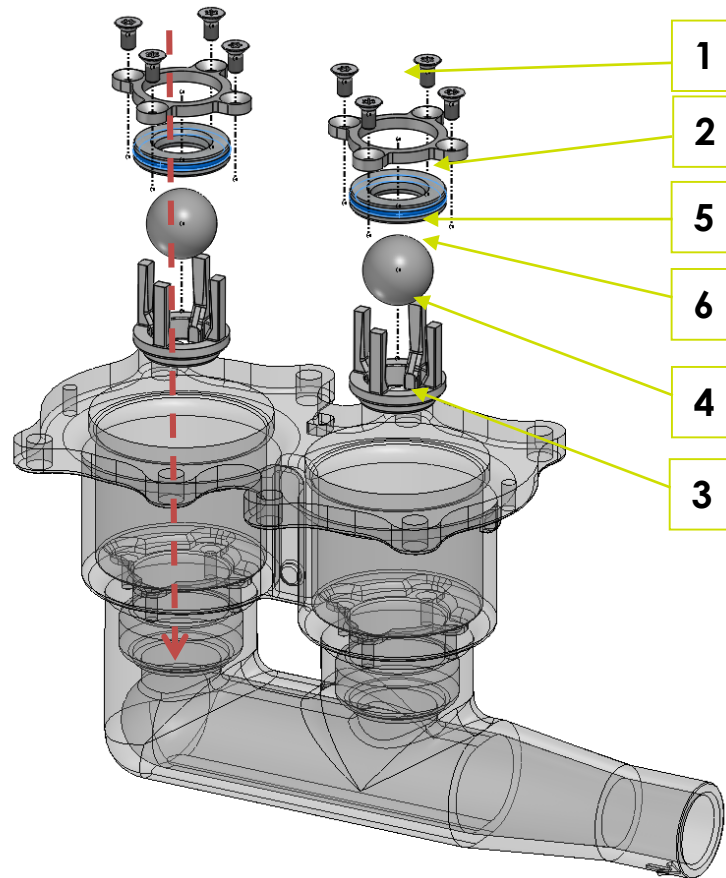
Assemblage des clapets produit dans le bloc cylindre
